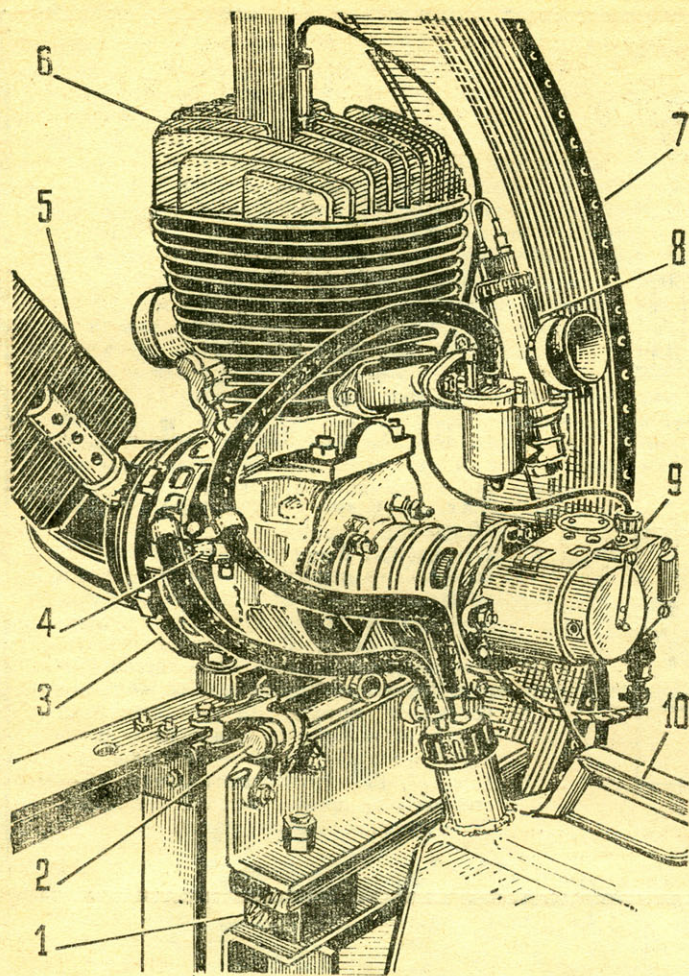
Винтомоторная установка «Оленя»: 1 — резиновый амортизатор, 2 — замок крепления к корпусу, 3 — генератор, 4 — шариковый клапан системы подачи топлива, 5 — воздушный винт, 6 — головка цилиндра, 7 — кольцевое ограждение, 8 — карбюратор К28Ж, 9 — магнето, 10 — канистра — топливный бак.
